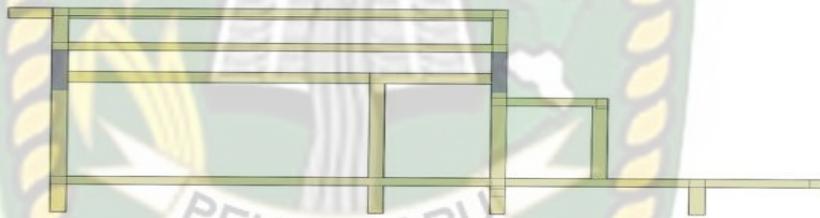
Mesin pengupas sabut kelapa tampak depan
